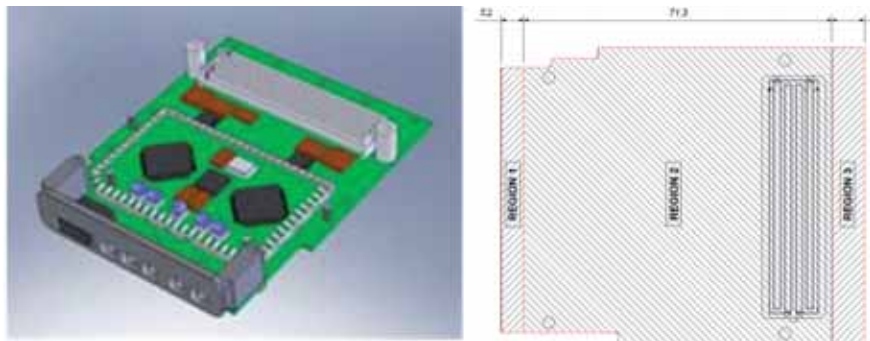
Disegno meccanico di un mezzanino FMC di dimensione singola (da [1])
